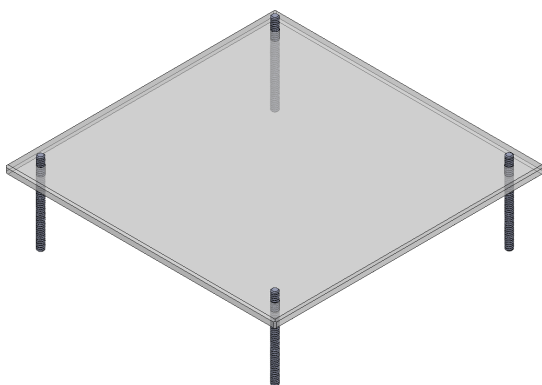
Plaque de fixation (vide et sans perçages) - Vue isométrique
